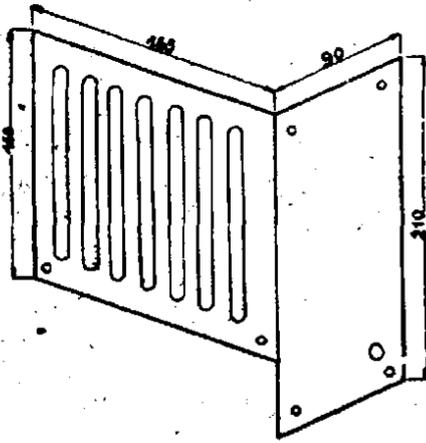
Vue en perspective de la partie mobile (arrière et flanc).
